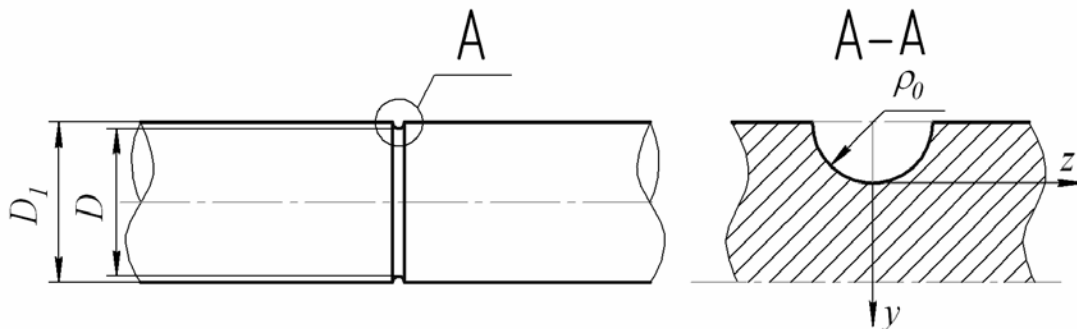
Рабочая часть цилиндрических образцов из стали 20 с надрезом полукруглого профиля для испытаний на усталость при изгибе
